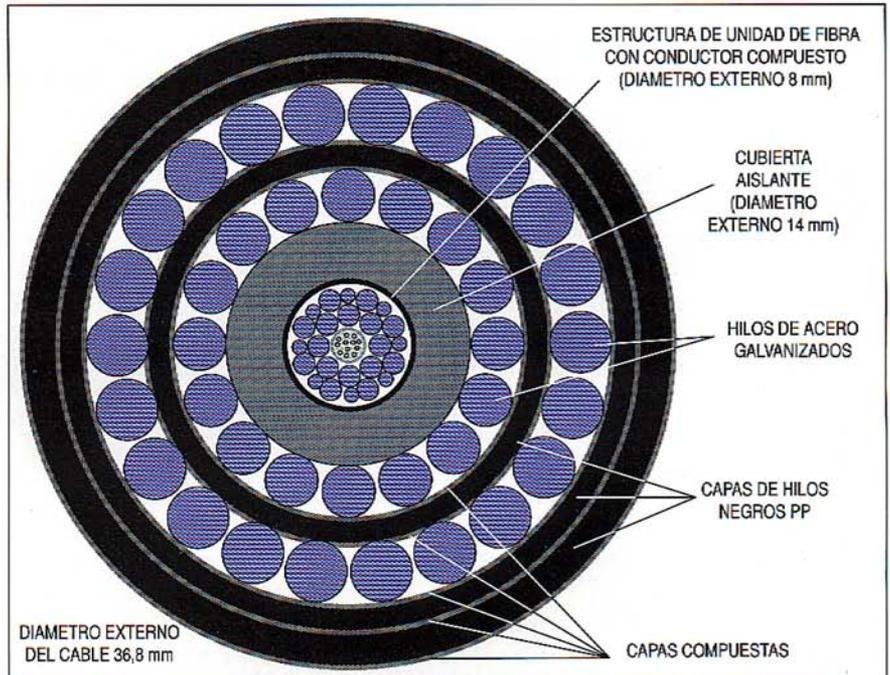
Sección transversal de un cable con minitubo de acero con armadura doble
